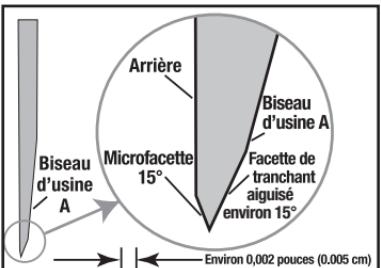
Coupe transversale du tranchant d'usine d'un couteau asiatique traditionnel typique grossi 50x (pour droitier).
